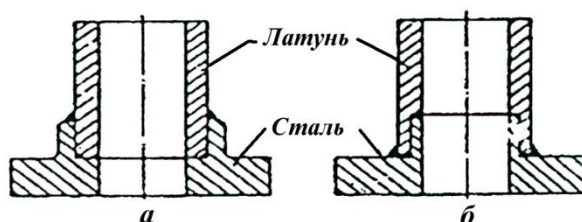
Соединение паянием двух трубчатых деталей из разнородных металлов.
